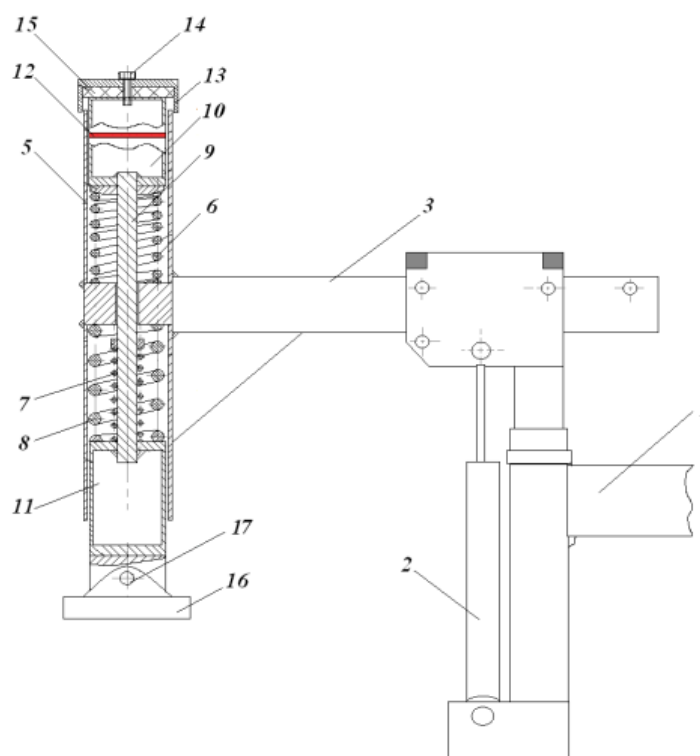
Схема прессующего механизма: 1 – рама; 2 – прессующий рабочий орган; 3 – поперечный брус; 4 – кронштейн; 5 – телескопический корпус; 6, 7, 8 – пружины, 9 – шток; 10, 11 – поршни; 12 – ограничитель; 13 – крышка; 14 – болт; 15 – проставка; 16 – упорная плита; 17 – соединительный палец
